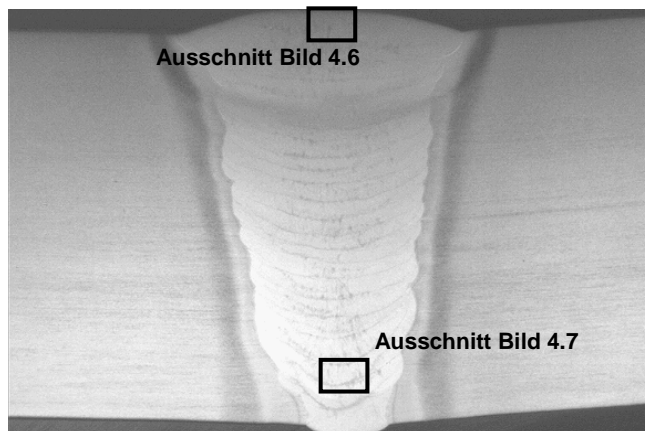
20 mm WIG-Engspalt-Schweißnaht
